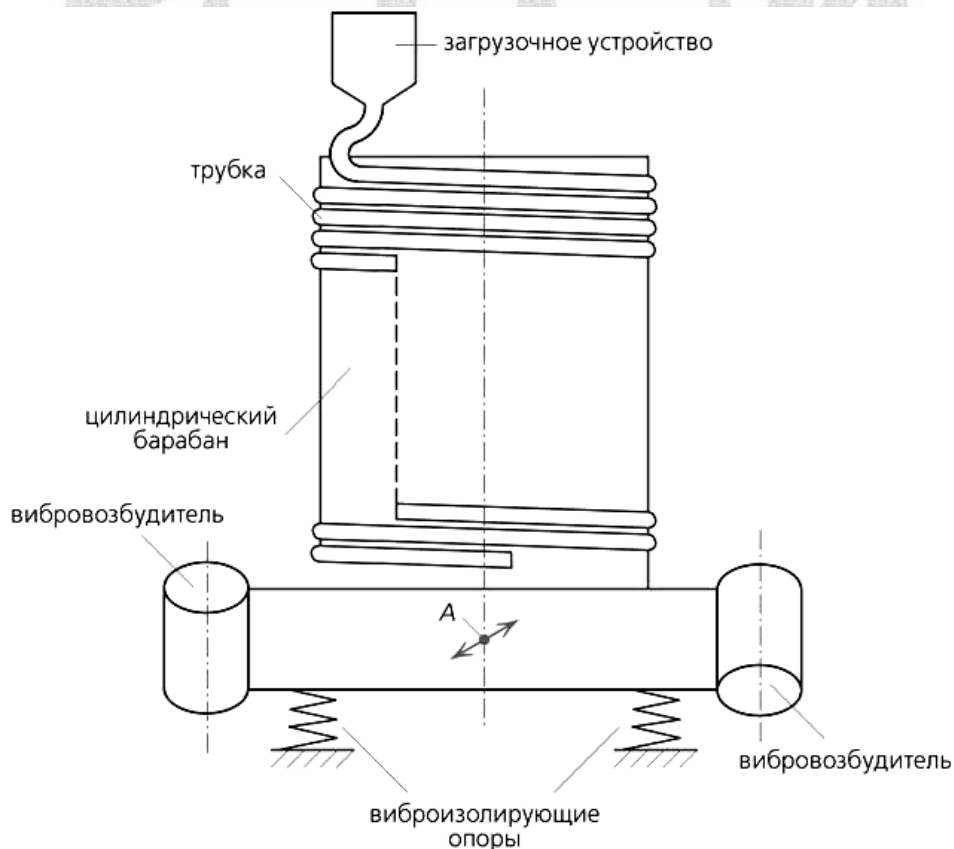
Схема устройства для заполнения порошком тонкой металлической трубки.
